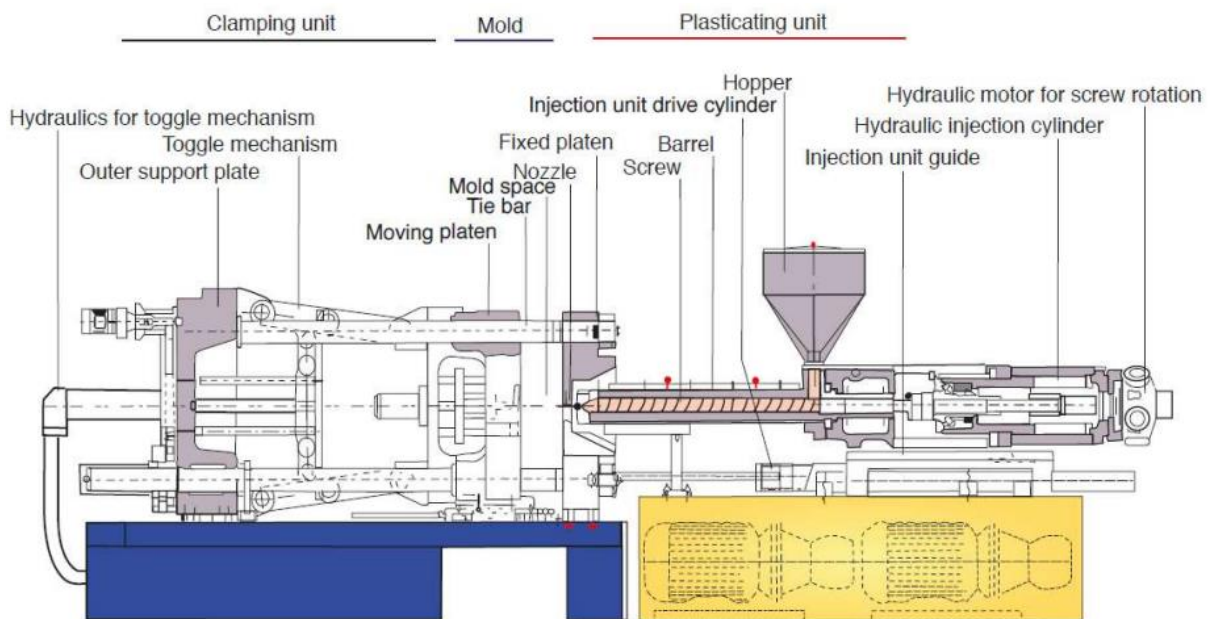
Componenti principali di una pressa per lo stampaggio a iniezione [15]
